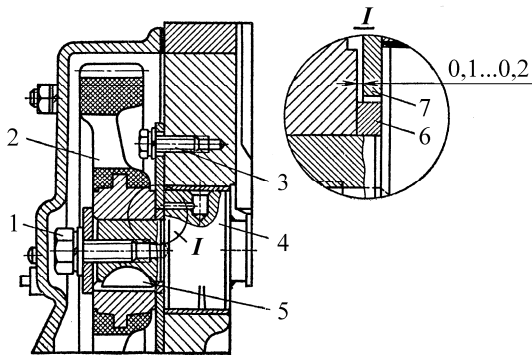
Носок распределительного вала и осевая фиксация: 1 – болт крепления шестерни; 2 – шестерня (текстолитовая); 3 – болт крепления упорного фланца; 4 – распределительный вал; 5 – шпонка; 6 – распорная втулка; 7 – упорный фланец
